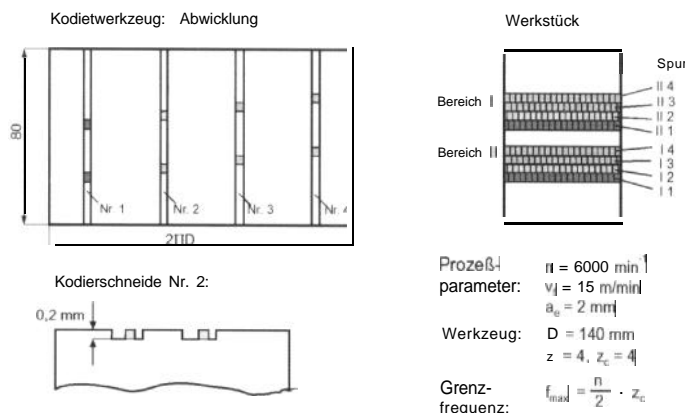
Kodierwerkzeug und entstehende Werkzeugoberfläche
